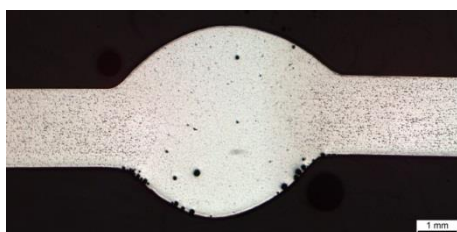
Микрошлиф сварного шва, $V = 4$ м/мин
